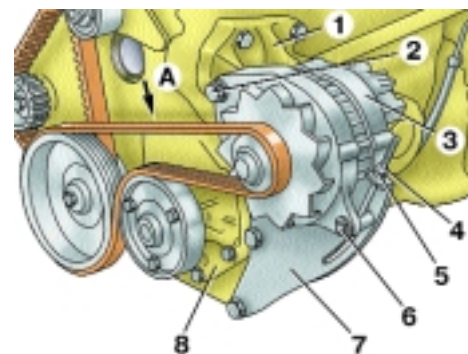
Привод вспомогательных агрегатов двигателя мод. F3R 272: 1 - кронштейн крепления генератора; 2 - болт крепления генератора к кронштейну; 3 - генератор; 4 - контргайка; 5 - гайка натяжителя; 6 - болт натяжителя; 7 - кронштейн натяжителя; 8 - водяной насос; А - место контроля натяжения ремня
